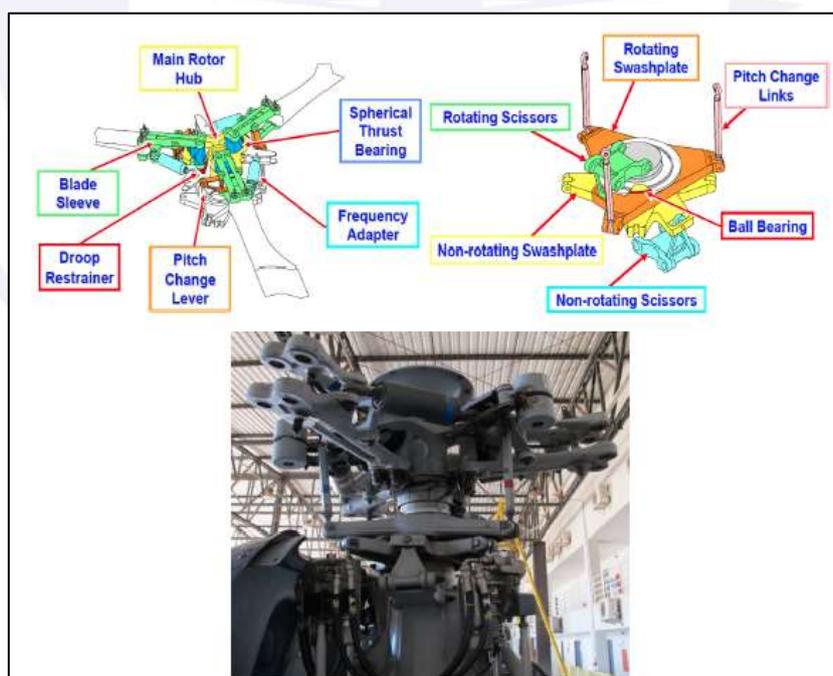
Main Rotor Head (MRH) and Main Rotor Shaft (MRS).
